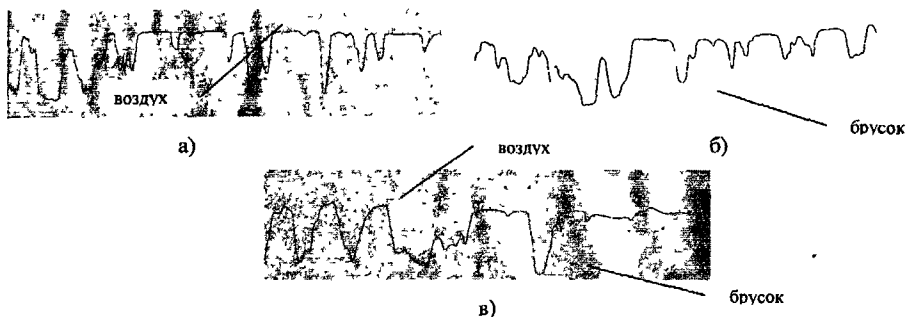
Профиль рабочей поверхности брусков ОКАИ
